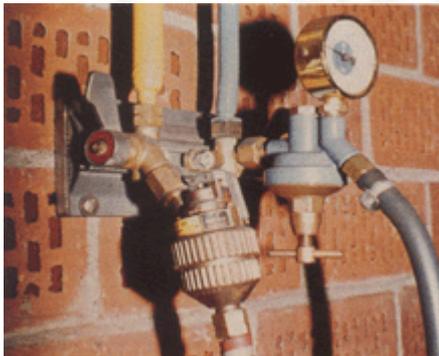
Schallabsorbierend gestaltete Wand in einer Schweißerei
